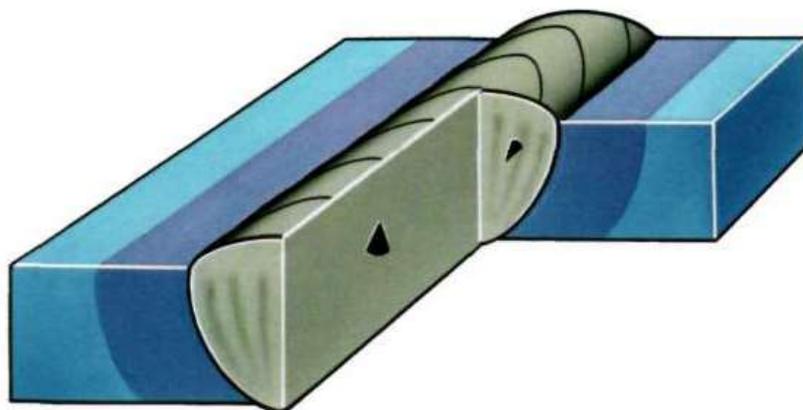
Дефект сварного шва по типу наличия твердых включений
